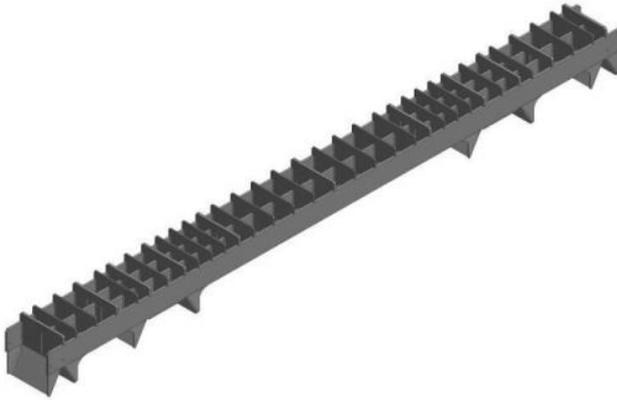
Geschweißtes Paddel mit 200 mm Sieblochung.
